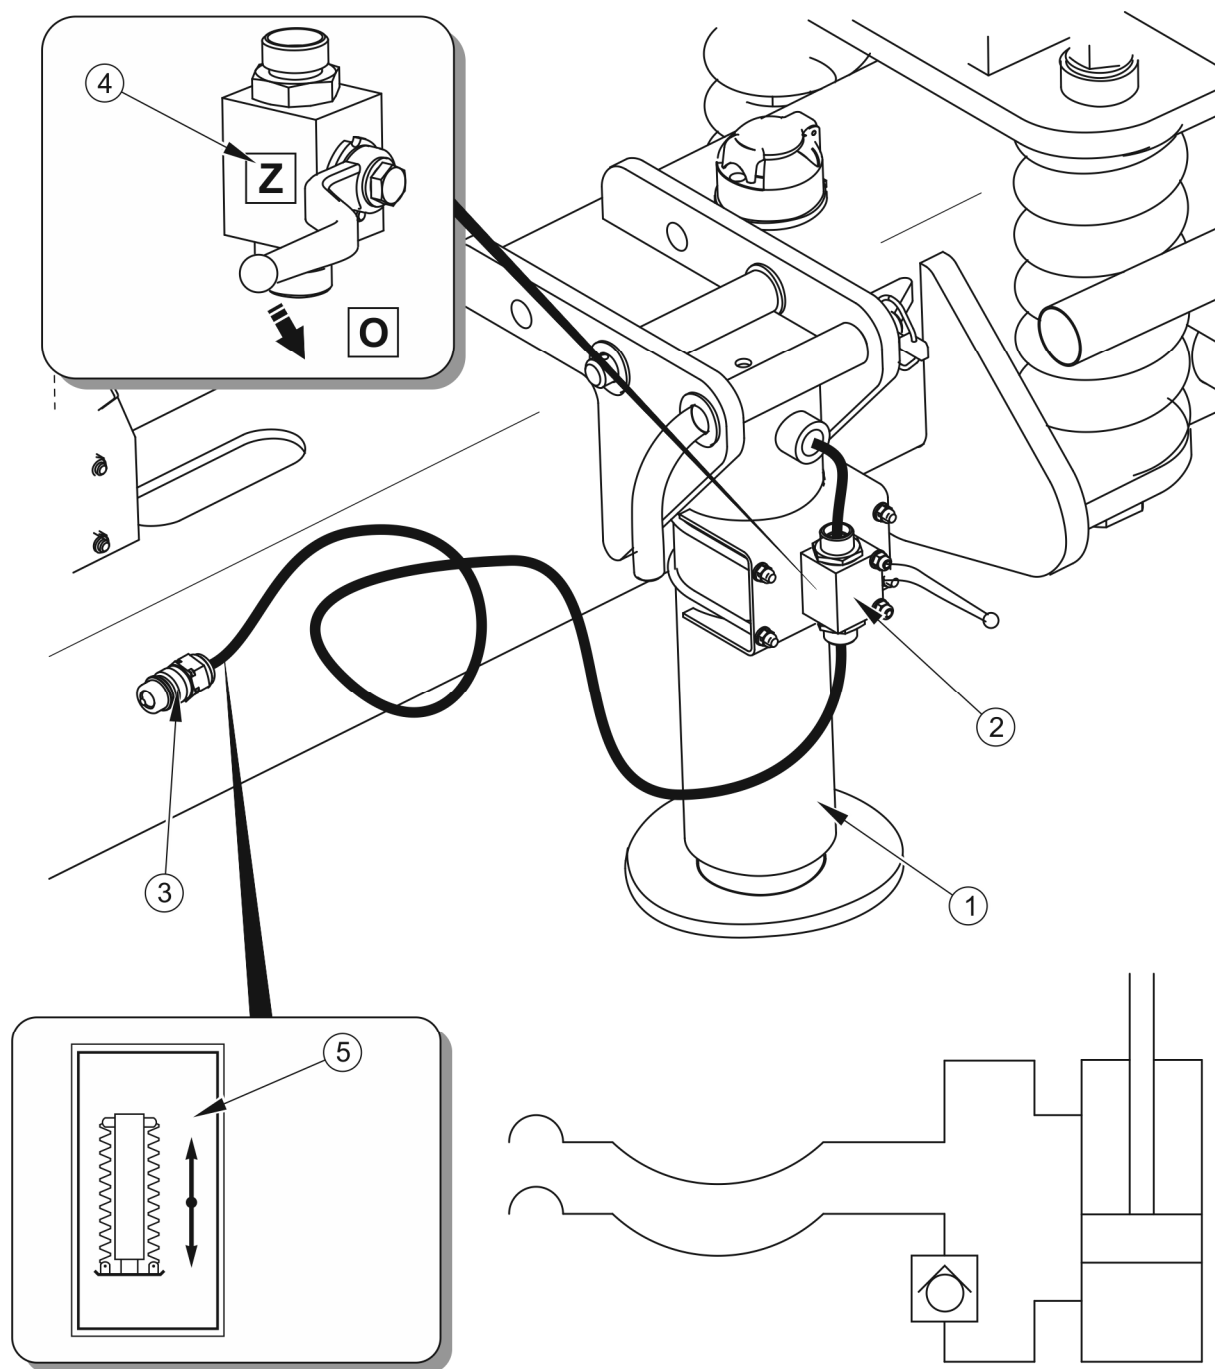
Konceptní návrh hydraulické instalace nájezdů
